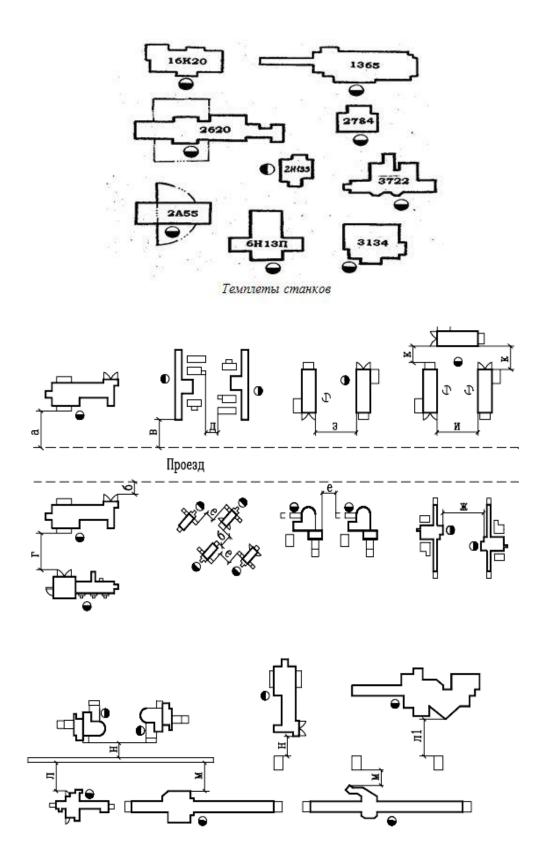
Расположение универсальных станков от проезда, относительно друг друга от стен и колонн здания
